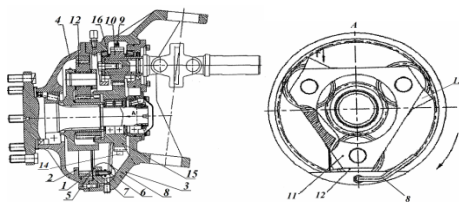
Планетарно-цилиндрический бортовой редуктора мобильной машины с насосом: 1, 2 - стенки, 3 - корпус редуктора, 4 - крышка, 5, 10, 15 - шестерни, 6 - штуцер. 7 - уплотнительный конус, 8 - трубопровод, 9 - форсунка, 11 - водило, 12 - сателлит, 13 - пластина, 14 - контрольная пробка. 16 - подшипник
